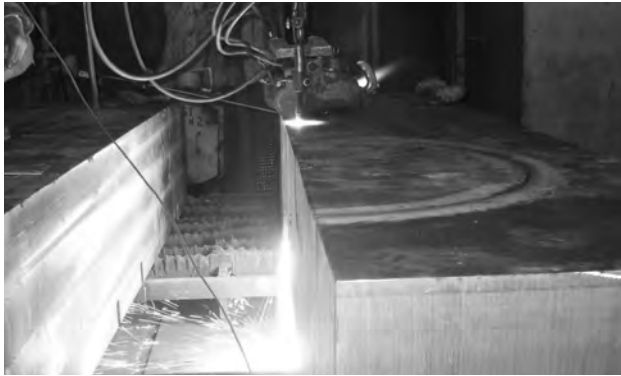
Выход кислородной струи из заготовки толщиной 450 мм по окончании фигурной резки
